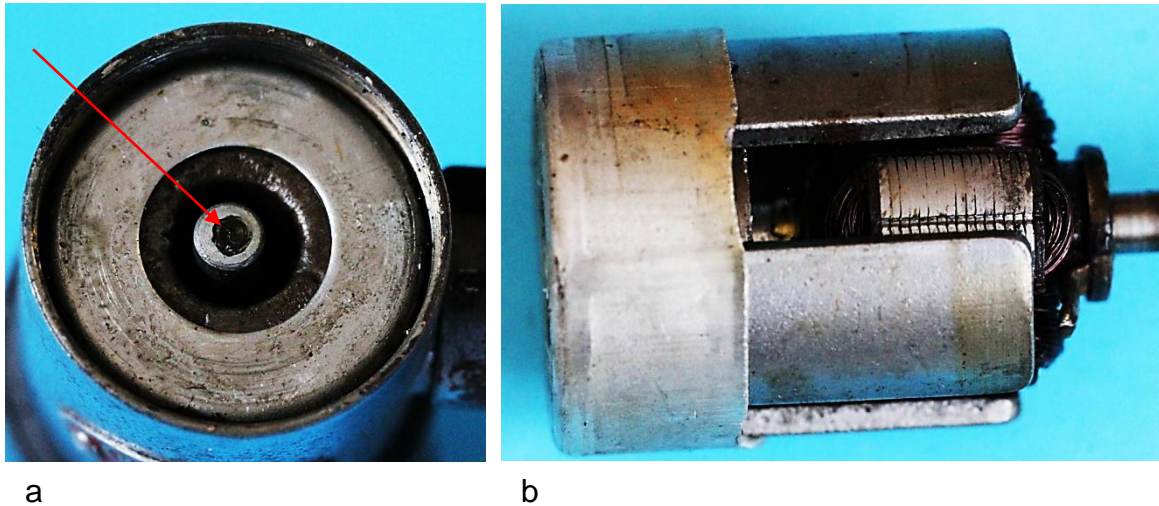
Generator: a) Eingebaut im Gehäuse, b) Magnetsystem und Anker
